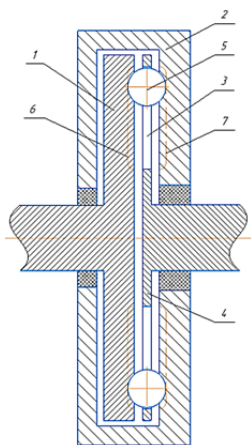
Схема торцевой цилиндрической передачи с ПТК
